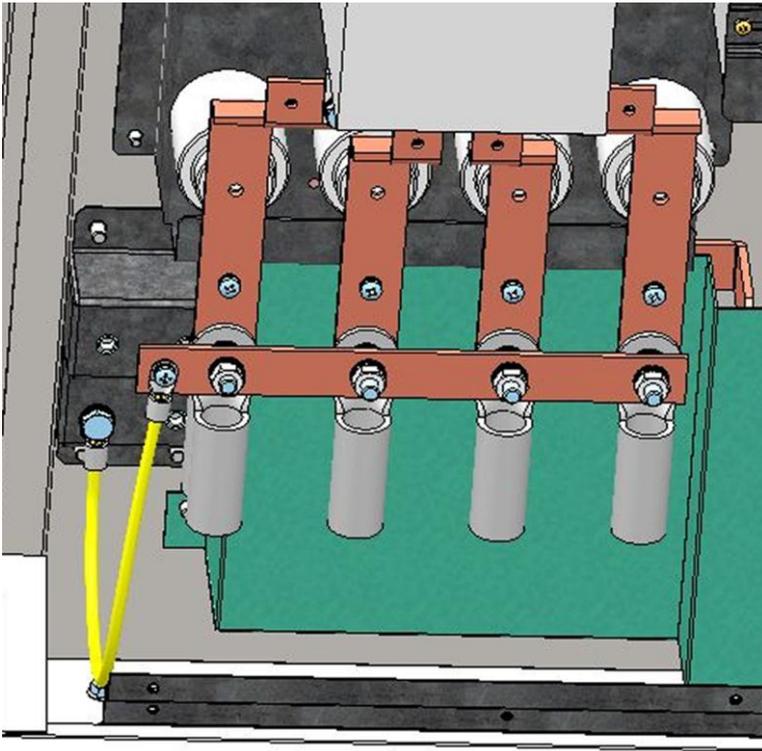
AC-Anschluss mit aufgeschraubter Kurzschluss- und Erdungsvorrichtung
